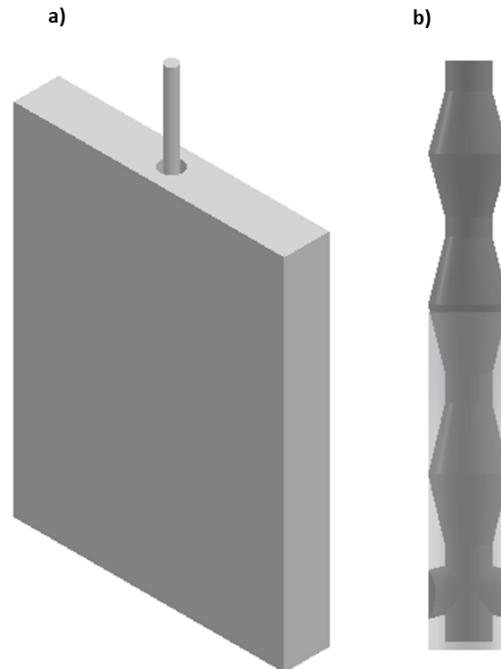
Geometrías modeladas en 3d. a) Molde y Buza, b) Buza desacoplada del molde.
